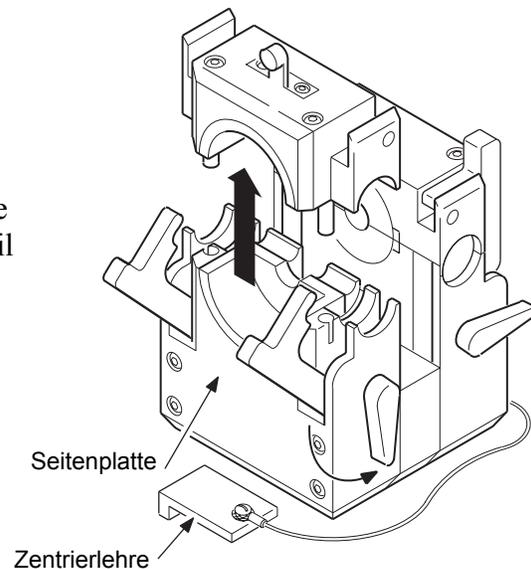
Entfernen des Oberteils der Seitenplatte
